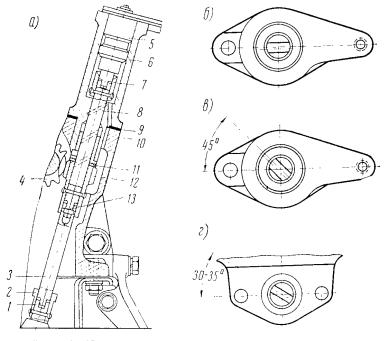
Привод масляного насоса и распределителя: 1 — валик масляного насоса; 2 — втулка; 3 — промежуточный валик; 4 — ведущая шестерия; 5 — распределитель; 6 — корпус привода; 7 — упорная втулка; 8 — валик привода; 9 — прокладка; 10 — блок цилиндров; 11 — упорная шайба; 12 — ведомая шестерия; 13 — штифт
